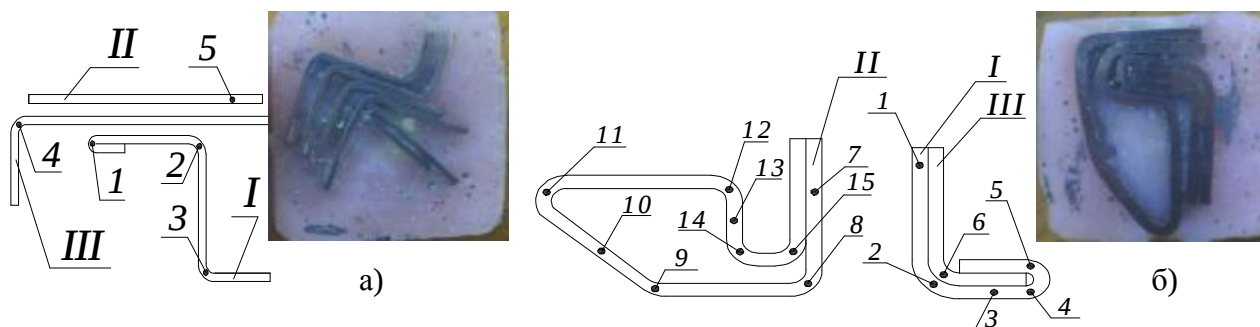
Точки замеров толщины заготовки на профилях и микрошлифы
